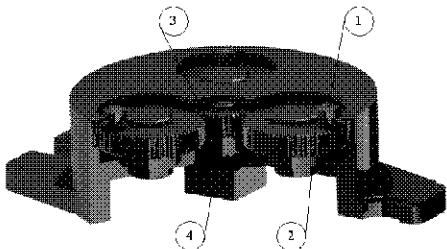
Переналагоджуваний базуючий модуль для установлення корпусних деталей у «координатний кут»
